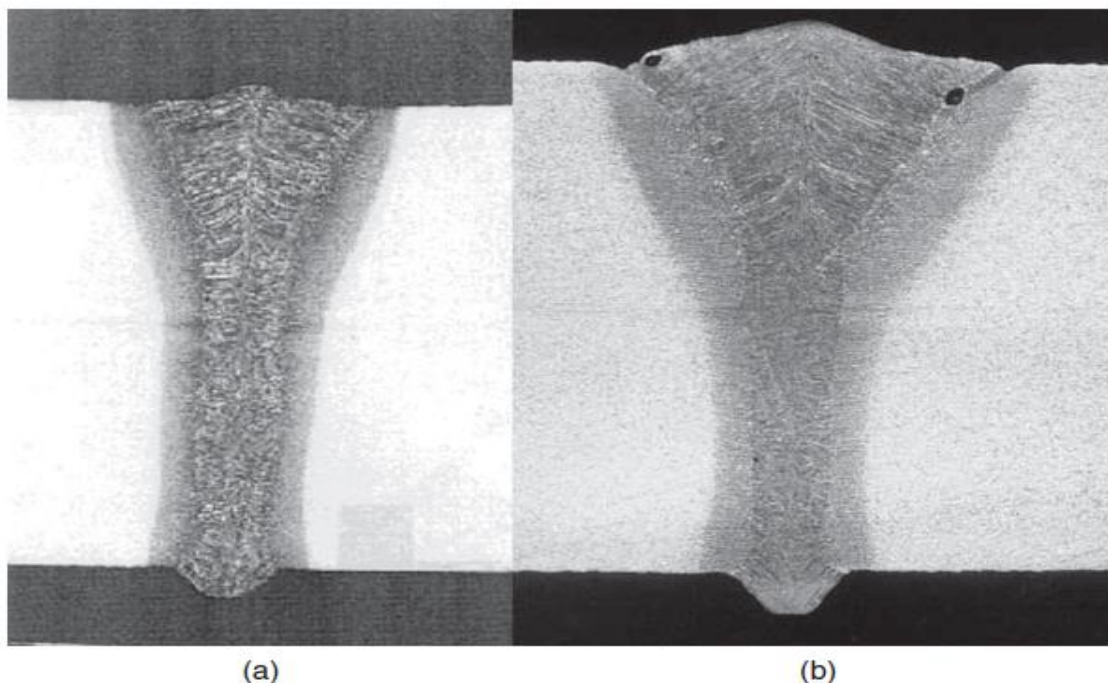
Sección transversal de acero estructural de 12 mm: a) soldadura láser (PL: 9kW, VS: 0.8 m/min, Gap: 0); y b) soldadura híbrida (PL: 11 kW, PA: 7.0 kW, VS: 1.4 m/min, VA: 15.8 m/min, Gap: 0.5 mm) (9)
